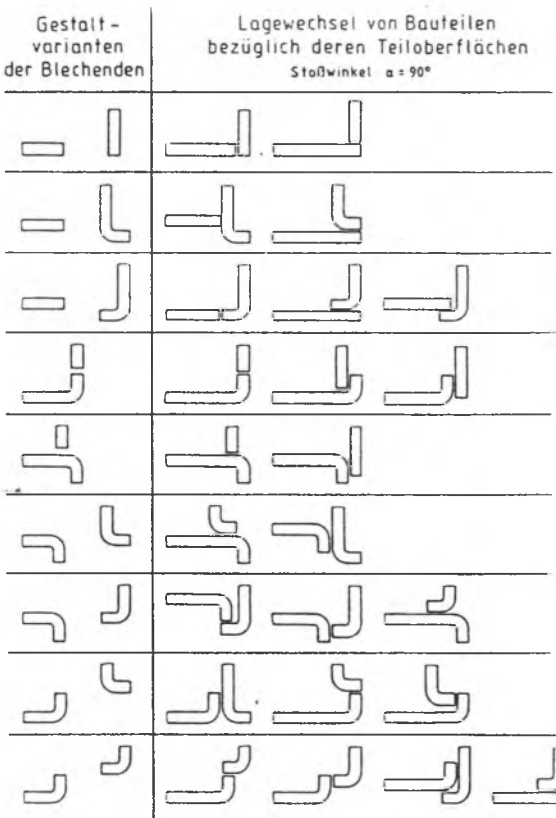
Varianten der Fugenlage dünner Bleche, entstanden durch Lagewechsel der Schweißbauteile bzw. Lagewechsel bezüglich Teiloberflächen der Schweißbauteile. Stoßwinkel der Bleche = 90° .
